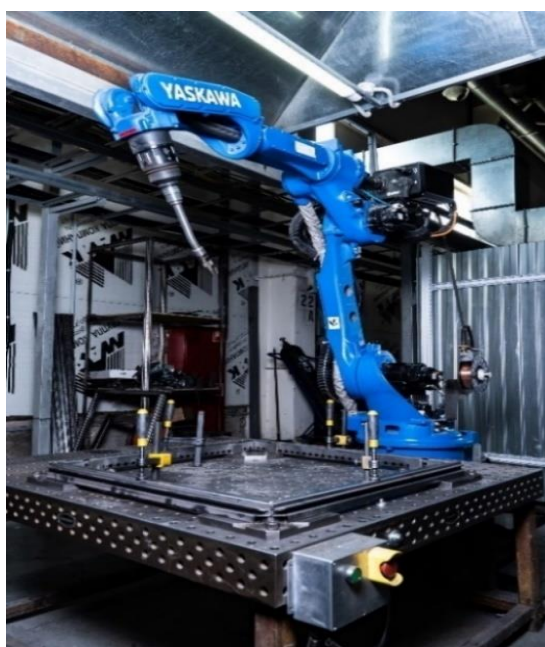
Сварочный комплекс Yaskawa
